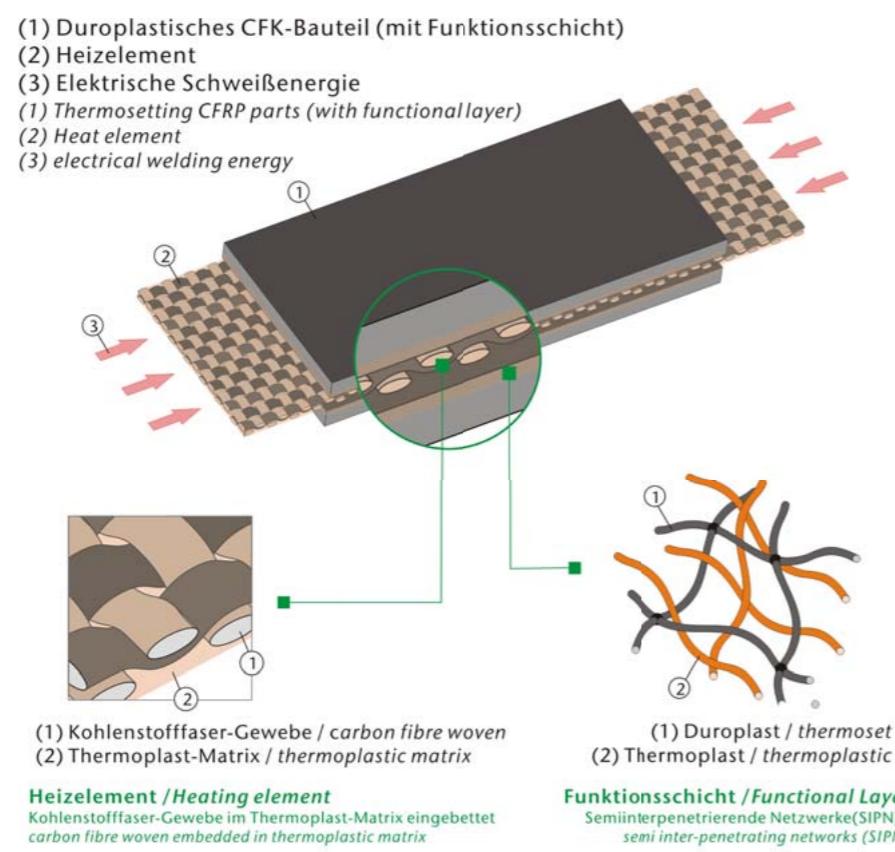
Prinzip des Widerstandsschweißens
